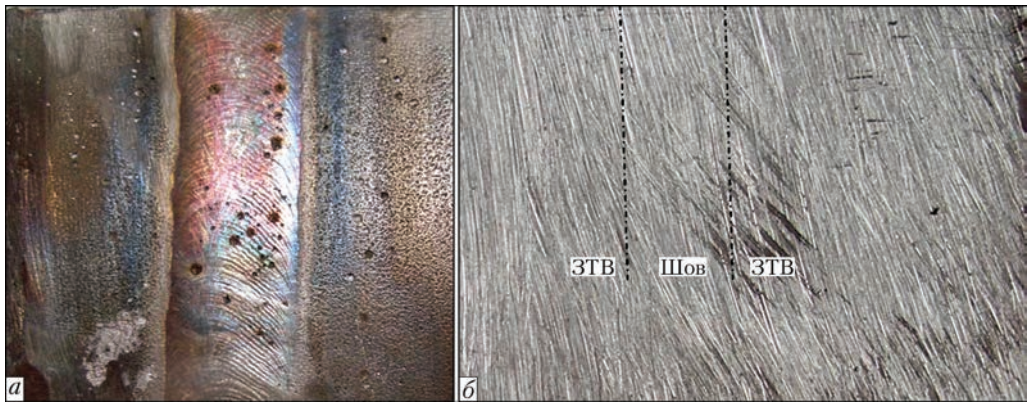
Поверхность сварного соединения листовой стали 12Х18Н10Т, испытанного на питтинговую коррозию в течение 5 ч в состояниях после сварки (а) и абразивной обработки (б)
